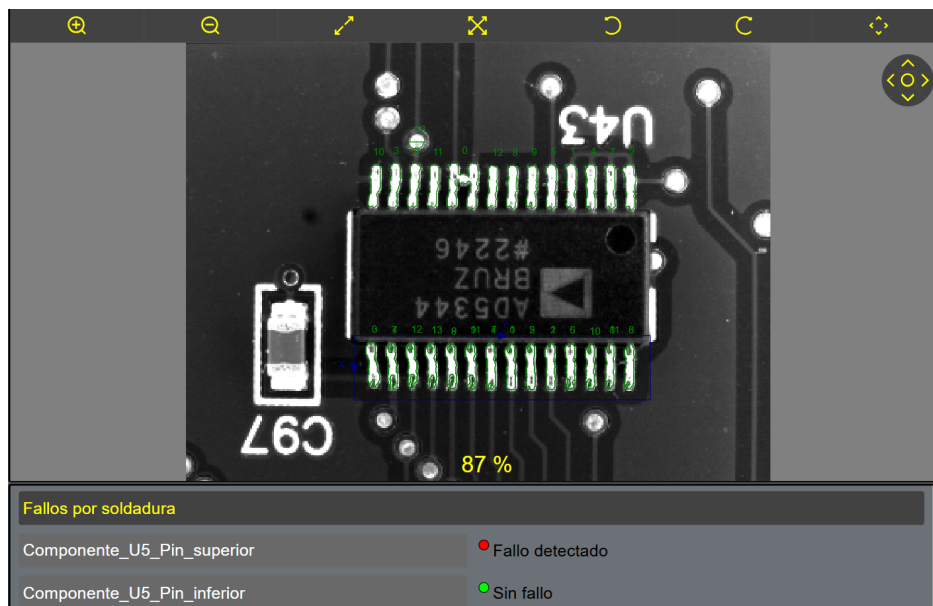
Inspección de componente U5. Fallo por bola de soldadura detectado. Cámara Insight 7200, programa Insight Visual Suite 5.9.0.
